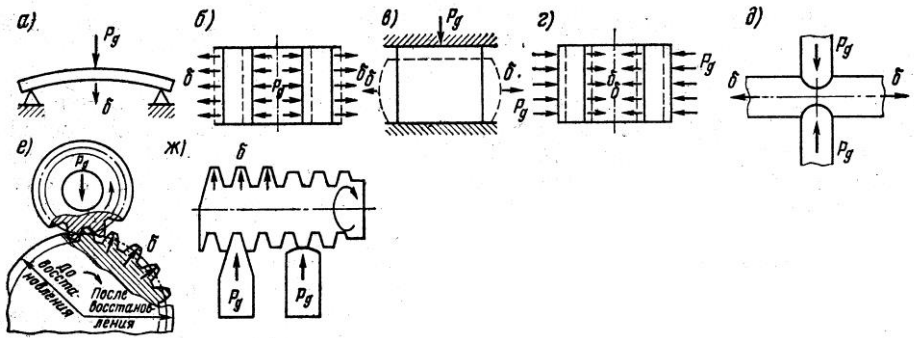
Схеми відновлення деталей тиском: а – правка; б – роздача; в – осадка; г – обтиска; д – витяжка; е – накатка; ж – електромеханічна висадка і зглажування
